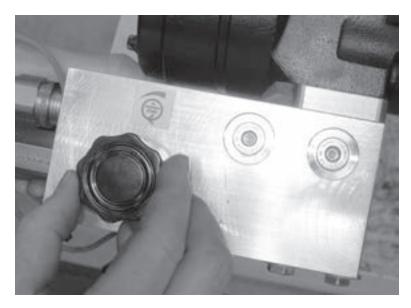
Utilisez la commande de vitesse sur le collecteur hydraulique pour régler la vitesse de rotation de la machine.
